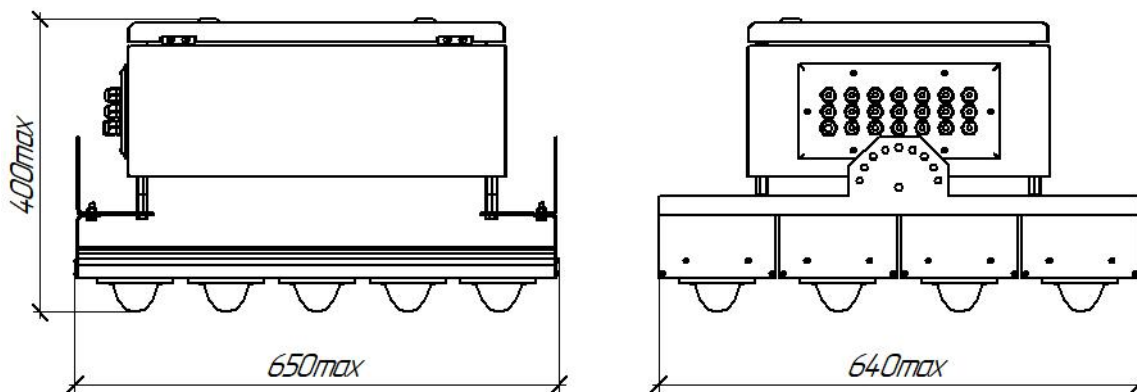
Габаритный чертеж прожектора PCSO-03-850-01,02-UHL1
